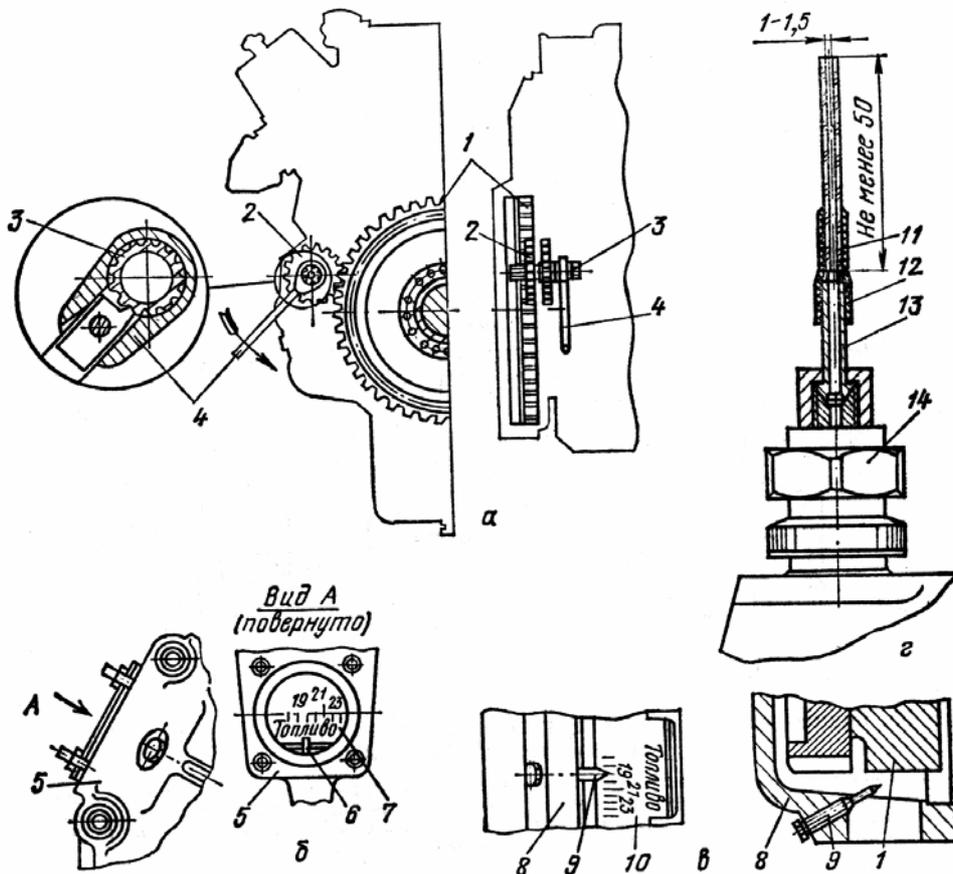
Механизм проворачивания коленчатого вала (а); метки гасителя крутильных колебаний (б) и маховика (в); установка моментоскопа (г):
